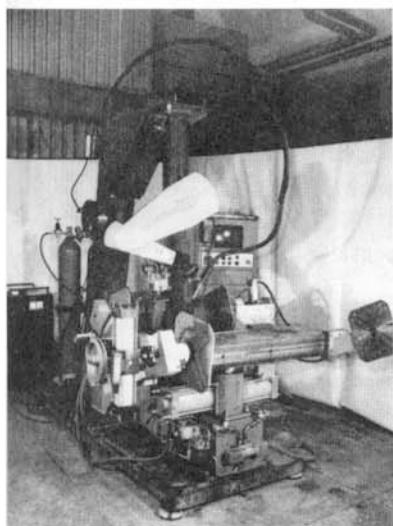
РТК с двухпозиционным поворотным столом с вращателем в каждой позиции для дуговой сварки конструкций небольших габаритных размеров
